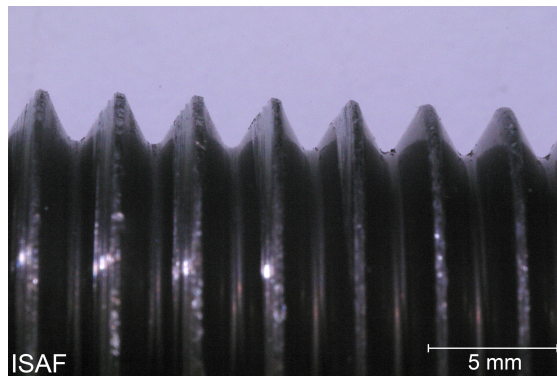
Gewindeprüfkörper axial belastet mit 40kN (Bolzen)
